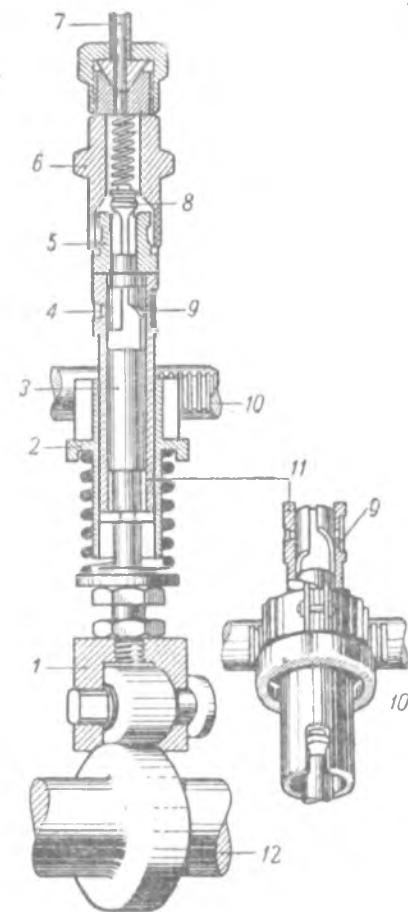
Секция топливного насоса: 1 — роликовый толкатель; 2 — втулка с зубчатым сектором; 3 — плунжер; 4 — всасывающее отверстие; 5 — седло нагнетательного клапана; 6 — штуцер нагнетательного клапана; 7 — трубка высокого давления; 8 — нагнетательный клапан; 9 — отсечное отверстие; 10 — рейка насоса; 11 — гильза плунжера; 12 — кулачковый валик насоса
